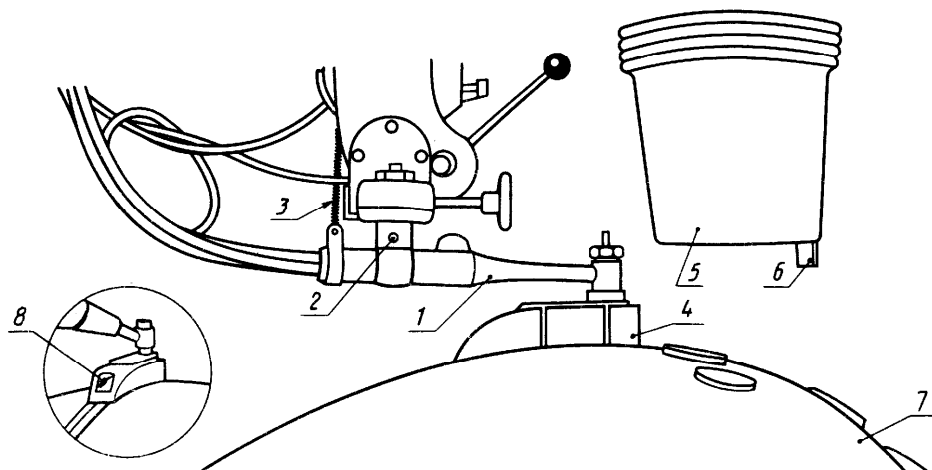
Установка для механизированной аргодуговой сварки деталей с криволинейным контуром
